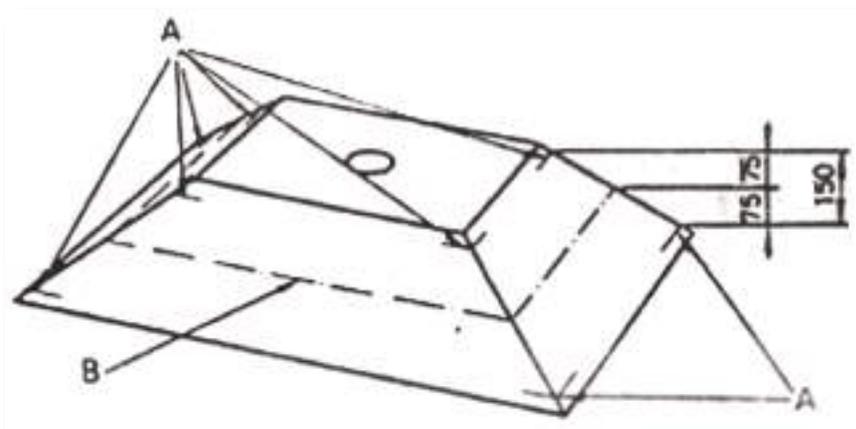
Pode ver-se nesta peça os traços A que delimitam os planos paralelos horizontais e o plano mediano B, traçado justamente a metade da distância entre esses dois planos.
